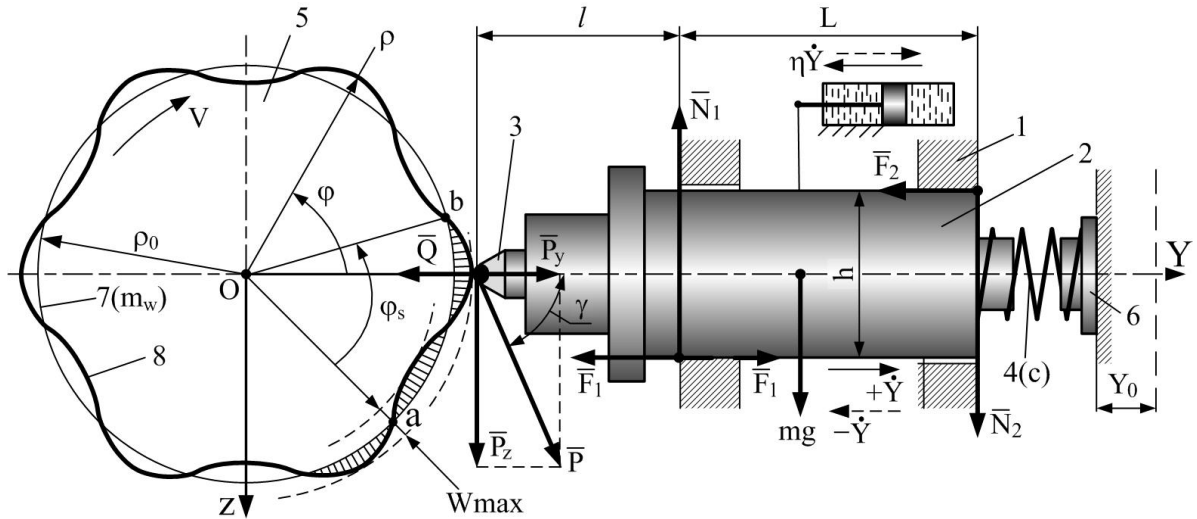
Модель процесса АВ наружной цилиндрической поверхности детали: 1 – корпус; 2 – ползун 3 – индентор; 4 – пружина; 5 – обрабатываемая деталь; 6 – подвижного упор; 7 – номинальный профиль поверхности детали; 8 – поверхность с отклонениями от круглости
